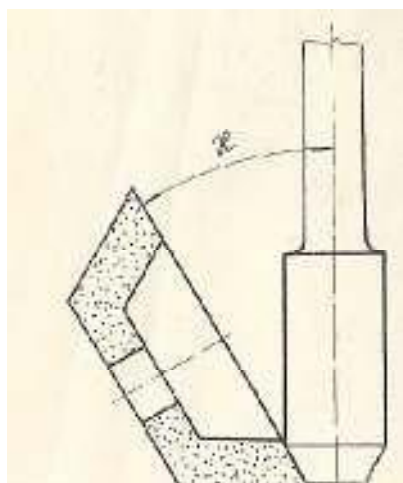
Prohlubování zubových mezer čelních zubů frézy.
